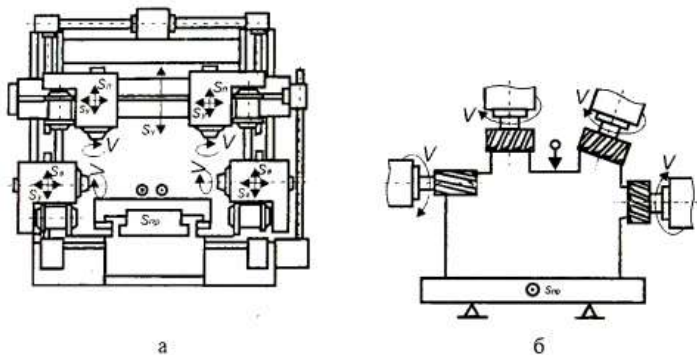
Загальний вигляд поздовжньо-фрезерного верстата (а) і схема фрезерування заготовки (б)
